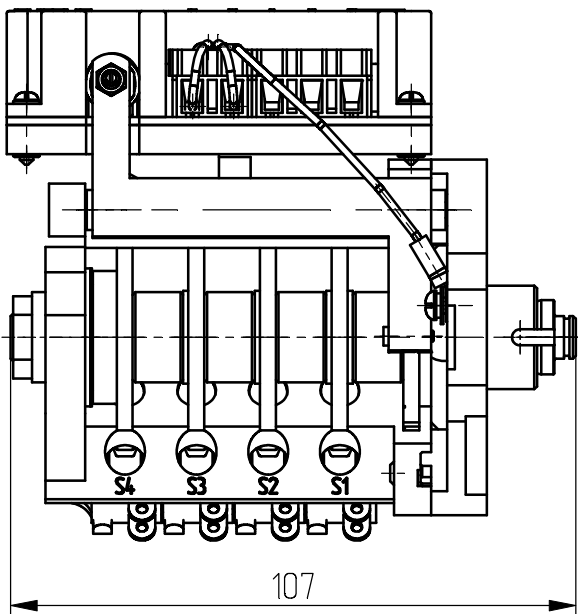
Общий вид, габаритные и установочные размеры блока БД-10АМК-0
